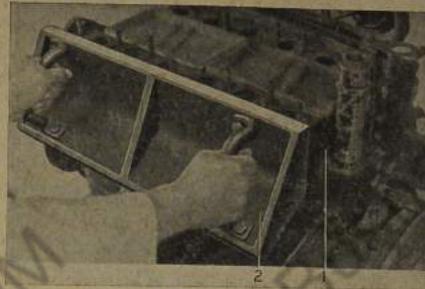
Tuschierplatte Nr. 1002 für Zylinder-Kurbelgehäuse
